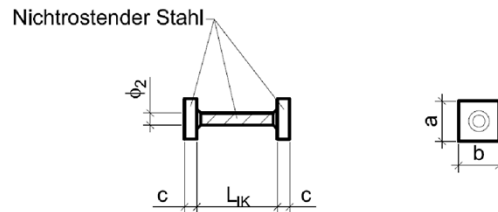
Druckelement aus Stahl mit angeschweißten Druckplatten, beidseitig bündig
